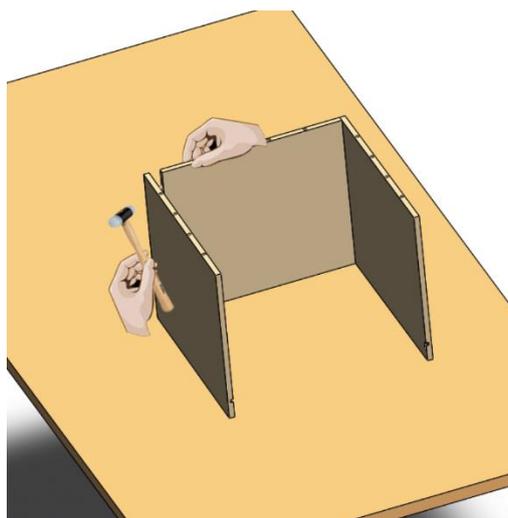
Paso 4 del ensamblaje del cajón (conjunto 2)
